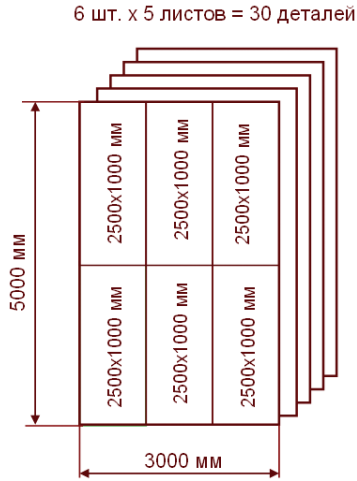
Желаемый вариант раскроя листового металла для изготовления 30 деталей
